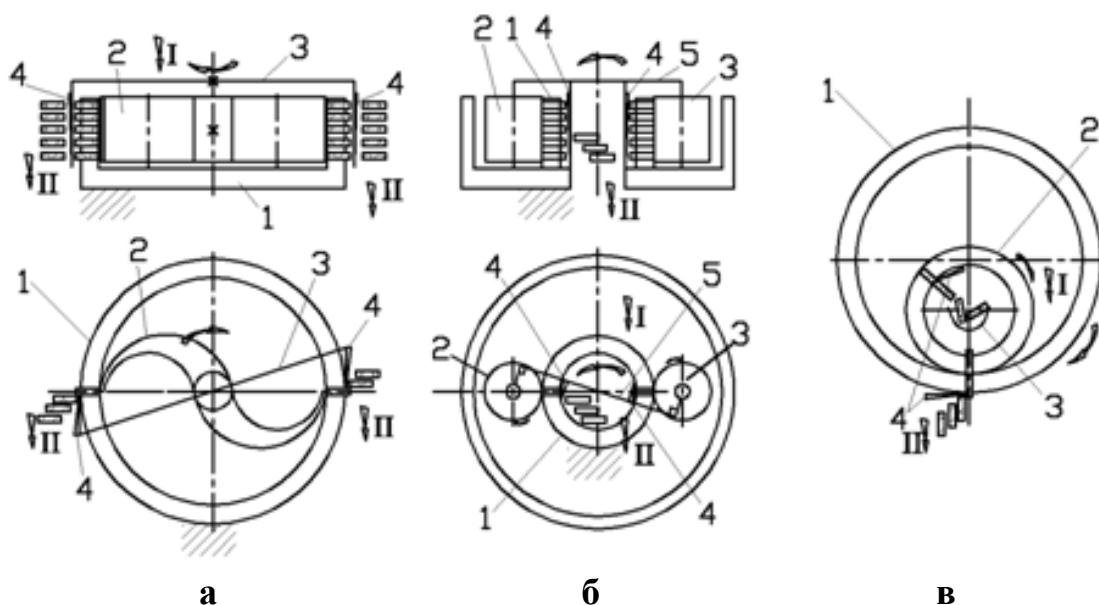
Схемы лабораторных прессов с кольцевой матрицей
